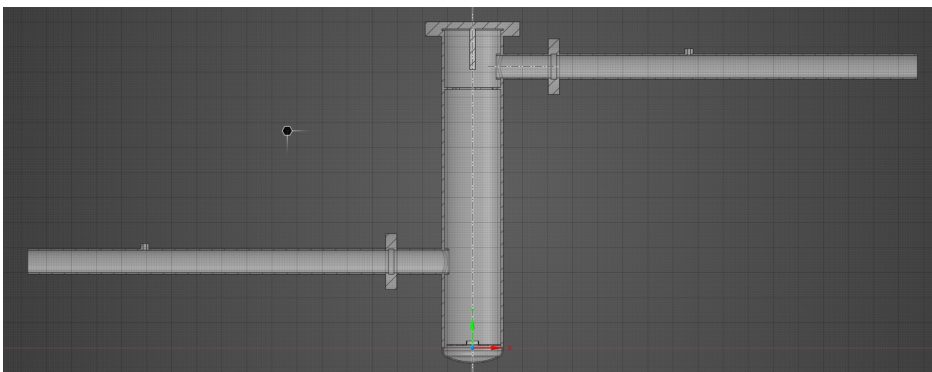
Vista in sezione longitudinale della geometria del corpo filtro
